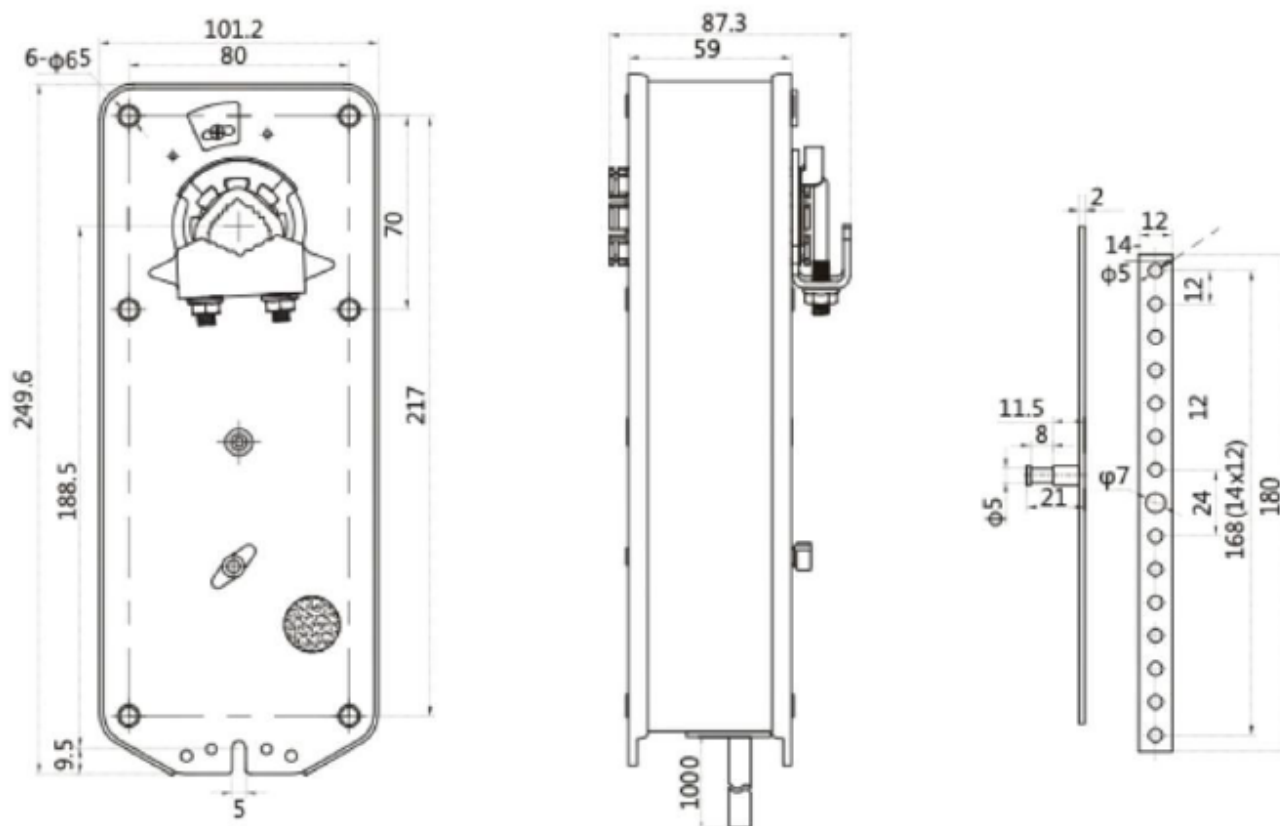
Общий вид и габаритные размеры электропривода VR10WS230-D(DS)
